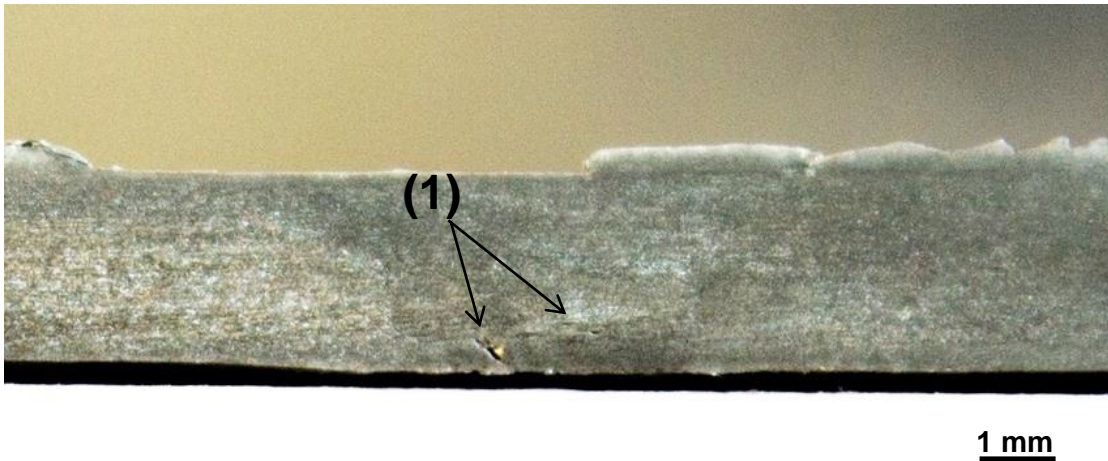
Seção da junta soldada com descida de 2,4mm da ferramenta.
